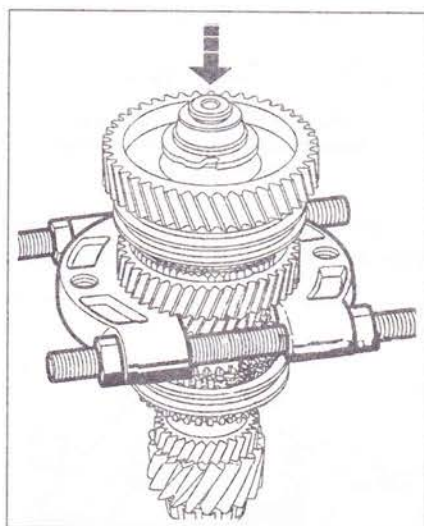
Снимите при помощи пресса сборку «кольцо-шестерня-муфта», упираясь съемником под шестерню 2-й передачи.
